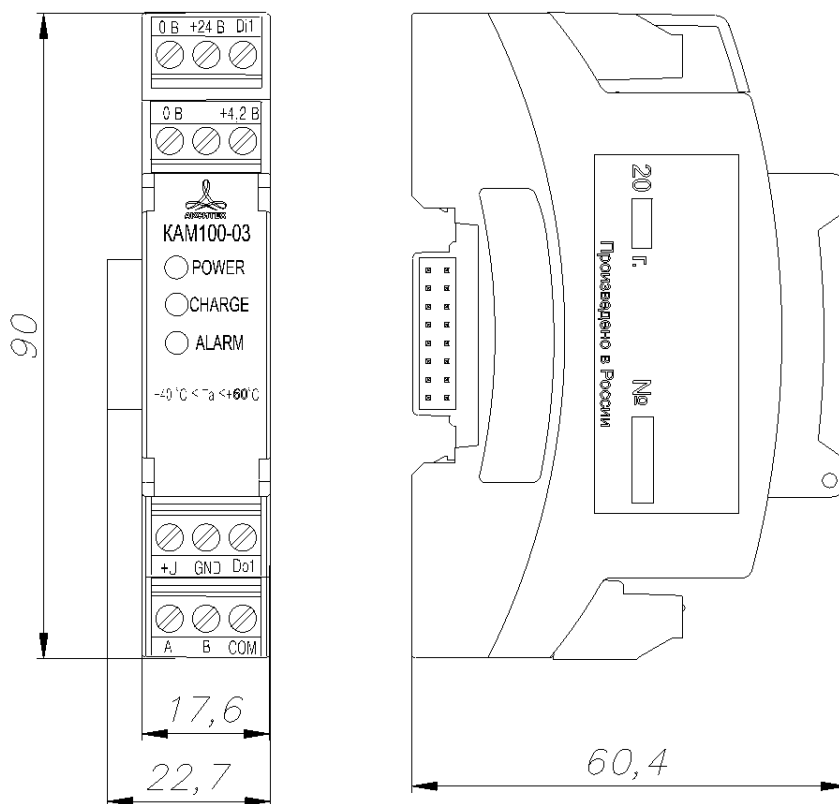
Внешний вид и габаритные размеры модуля контроля заряда KAM100-03
